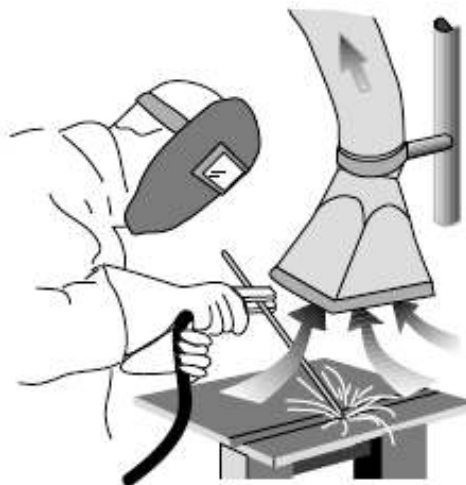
Uso de extractores de vapor al soldar¹⁰⁶
